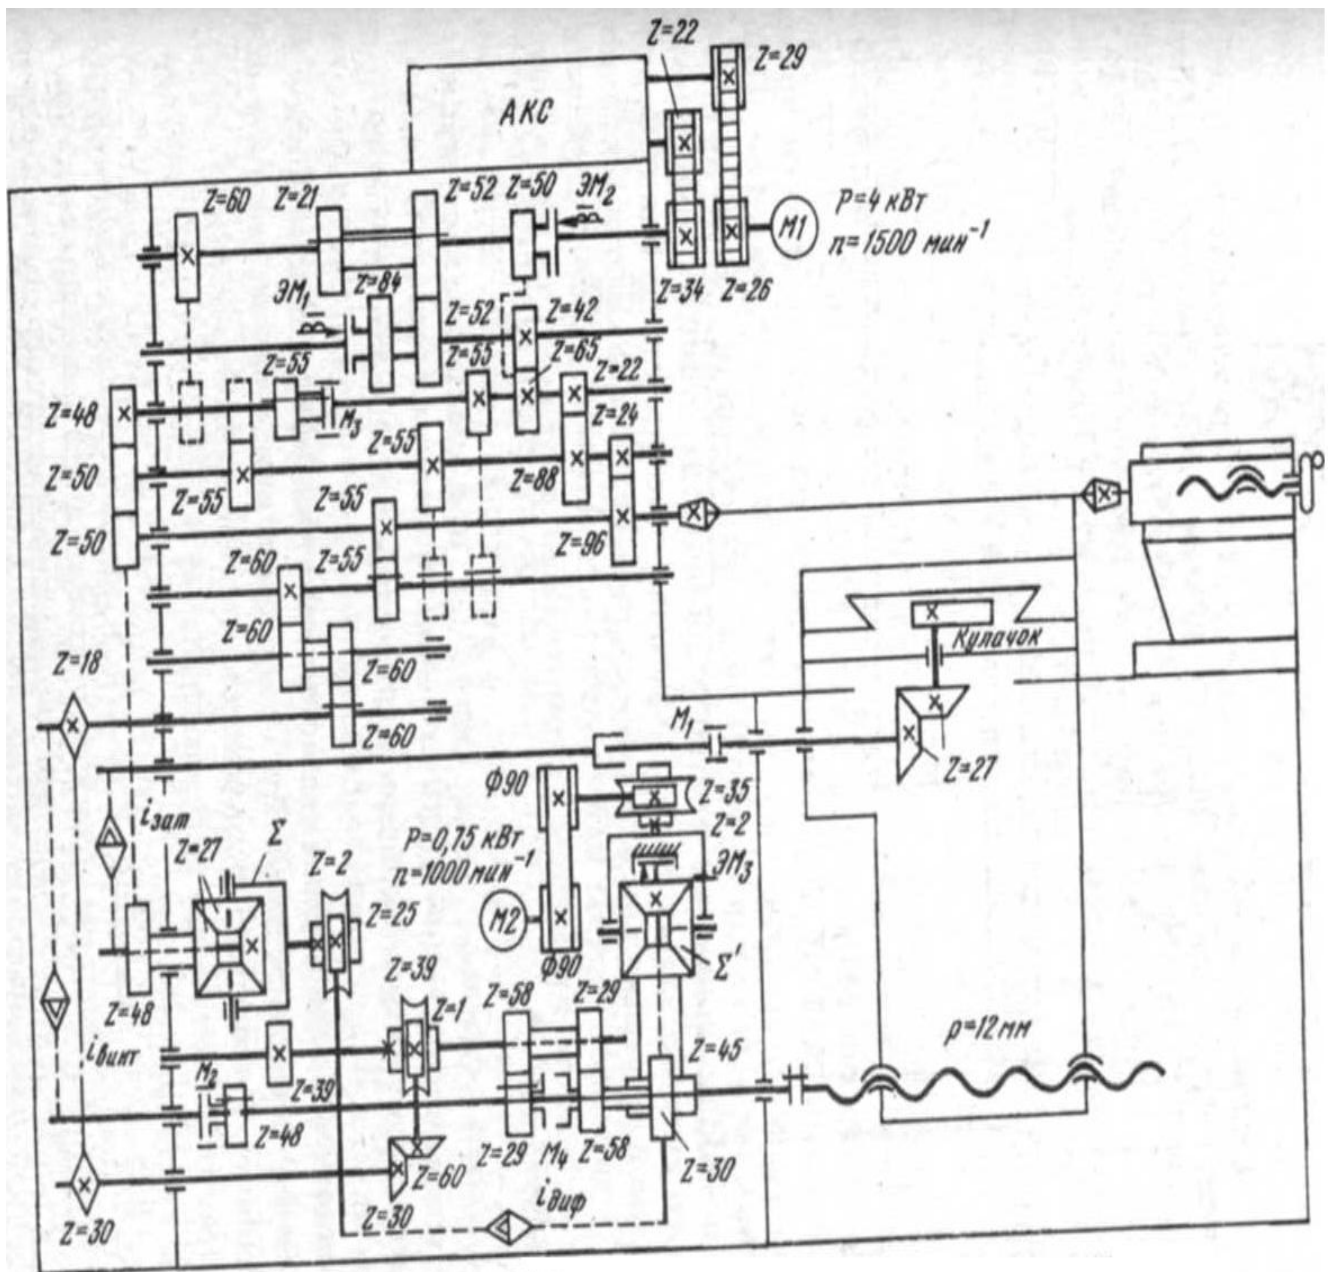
Кинематическая схема универсального токарно - затыловочного станка модели 1E811.
